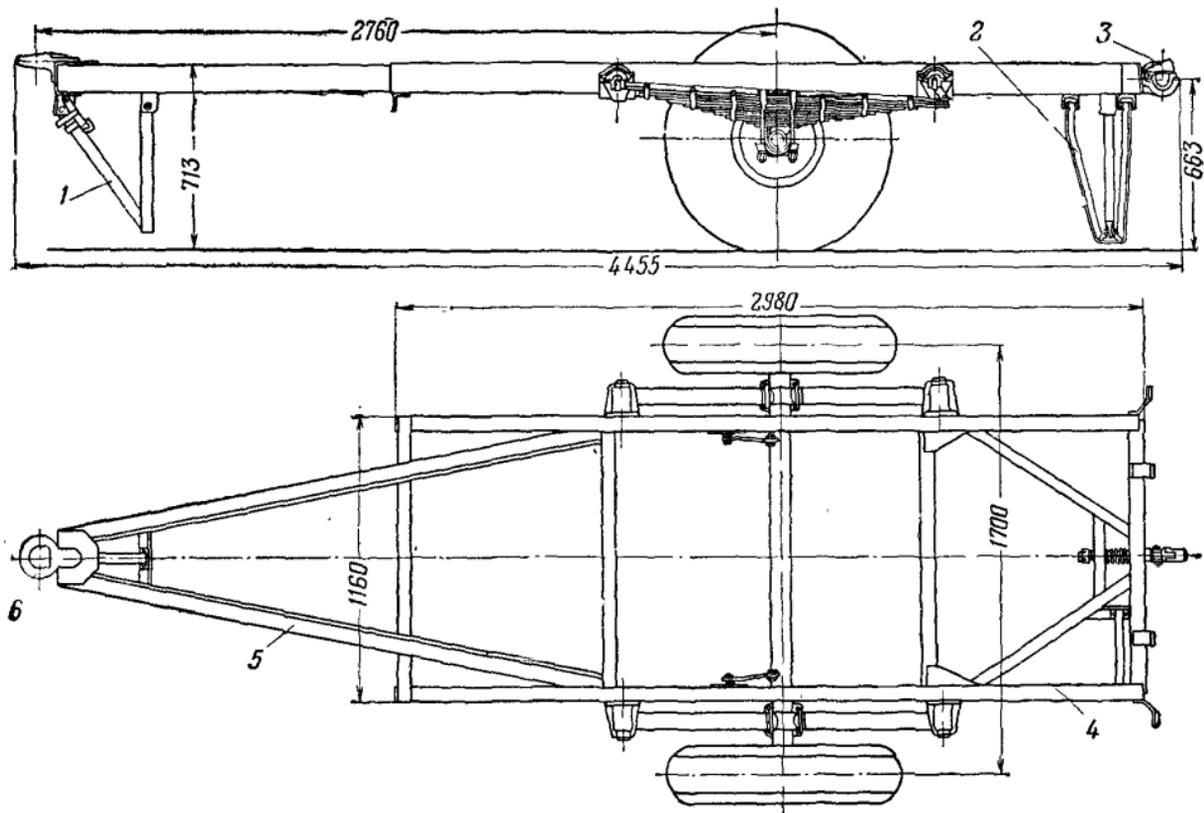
Общий вид прицепа 1-П-1 (ЛАЗ-712);
